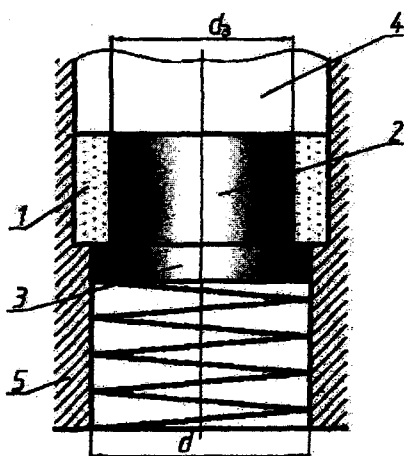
Схема нанесения обмазки на поверхность заготовки
